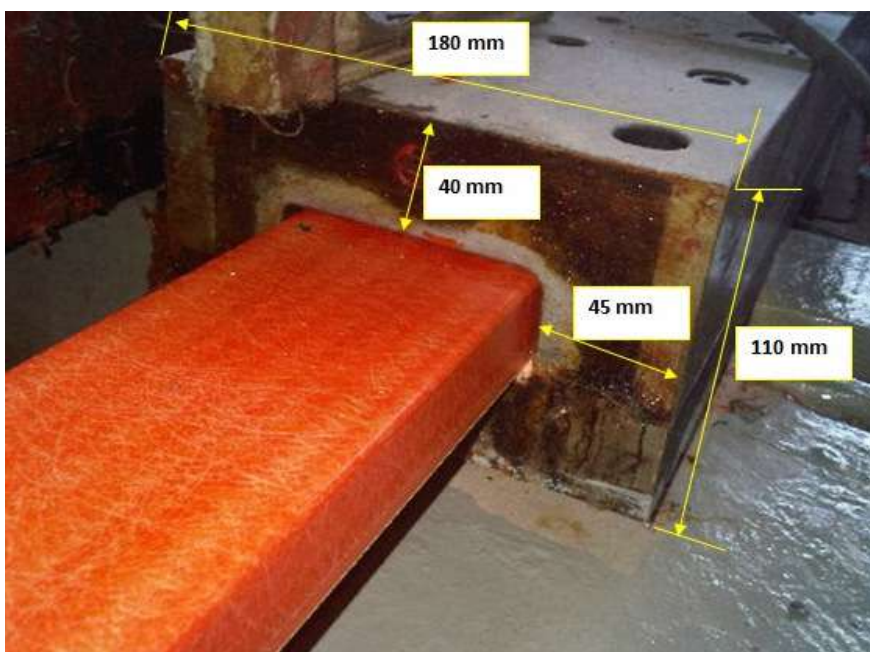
Dimensões da área transversal de geometria “C” do molde da empresa parceira.
